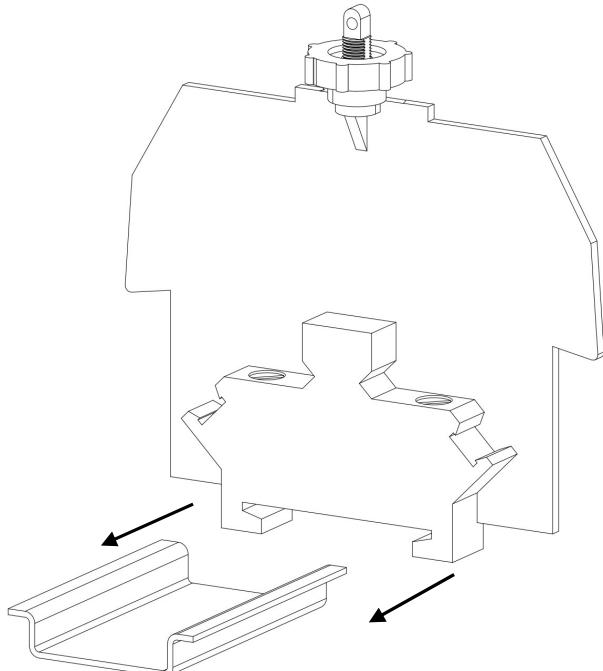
установка держателя защитного профиля со специальной ножкой
